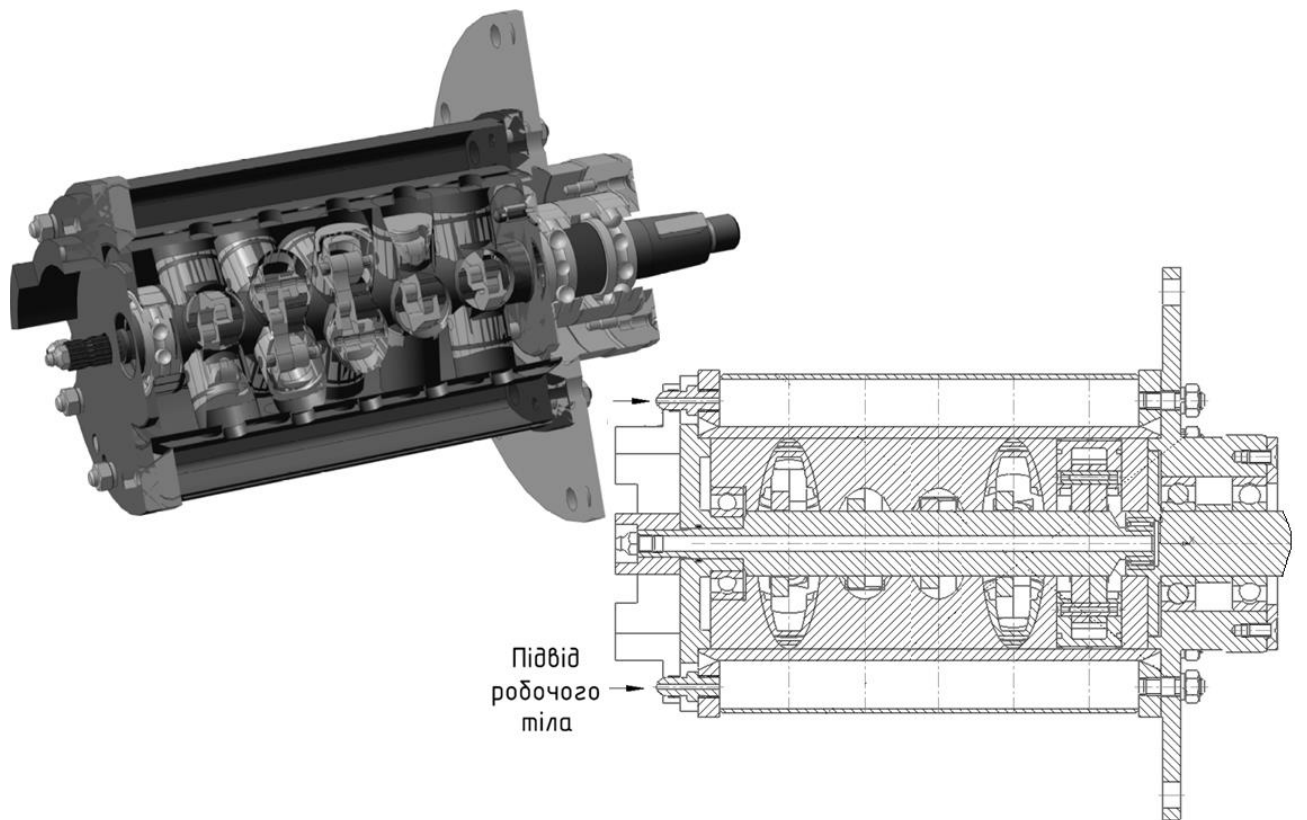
Корпус роторно-поршневого двигуна
